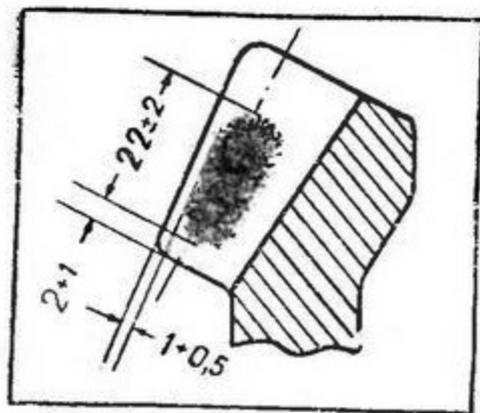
Расположение пятна контакта на зубе ведомой шестерни.
